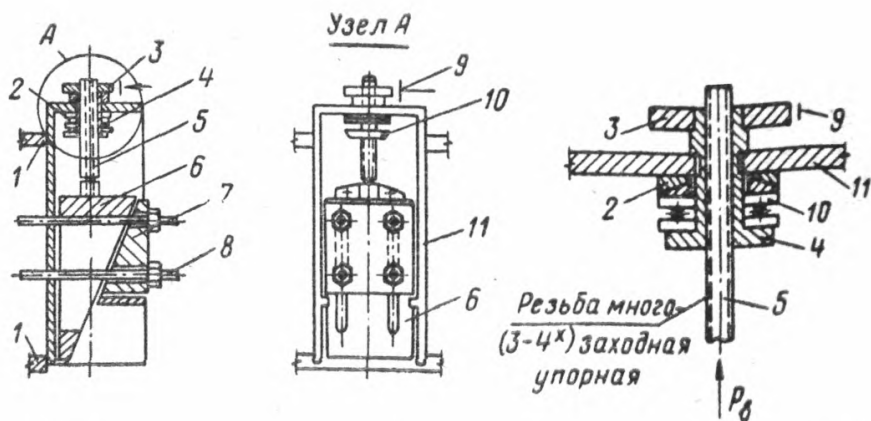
Клиновинтовое устройство для отпуска натяжения в арматуре (опыт Красноярского комбината железобетонных и металлических конструкций)
